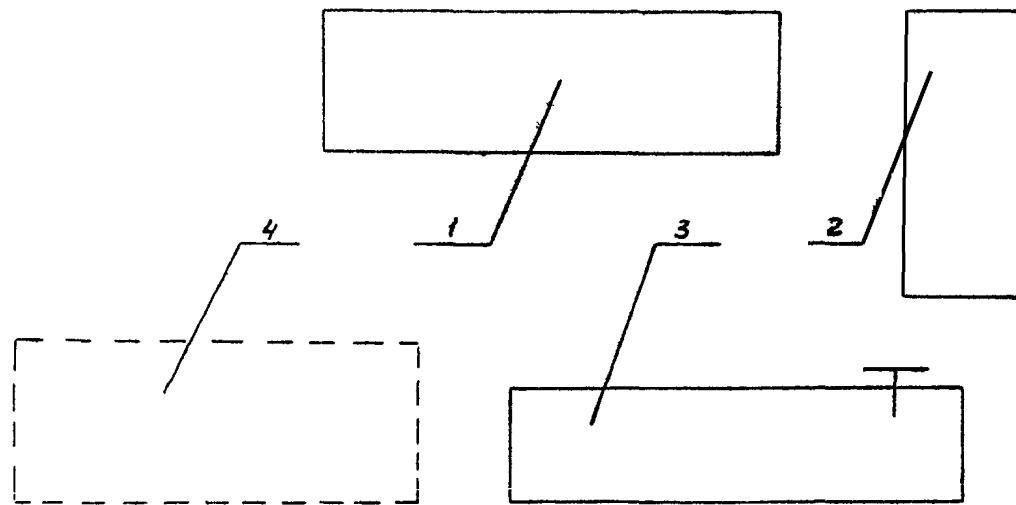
Типовая схема планировки рабочего места разборки и сборки механизма
